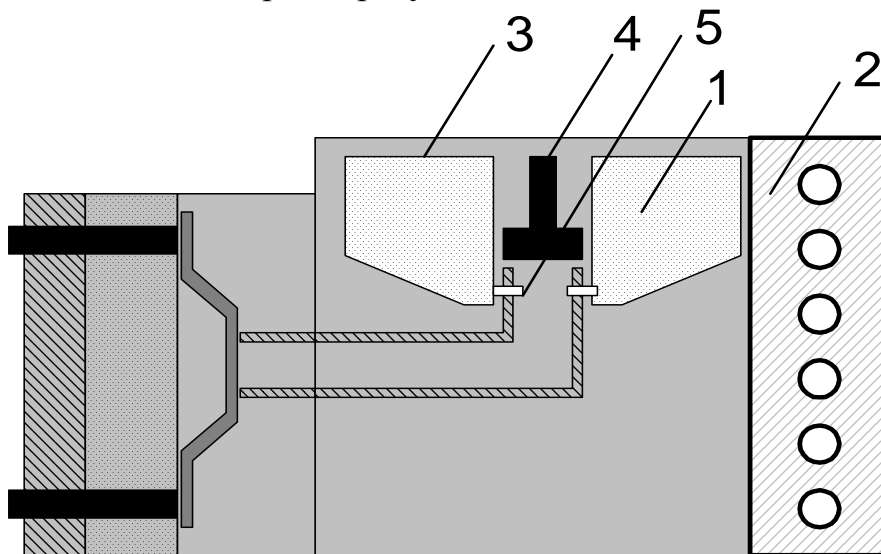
Ливарна машина з гарячою вертикальною камерою пресування
